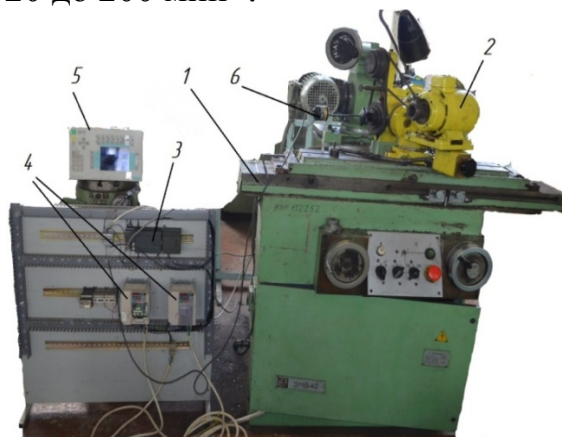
Универсально-заточной станок модели 3М642 с экспериментальным стендом: 1 - станок модели 3М642; 2 - приспособление для наружного круглого шлифования 3Е642Е.П17; 3 – промышленный контроллер; 4 – частотные преобразователи; 5 – операторская панель; 6 – энкодер.
